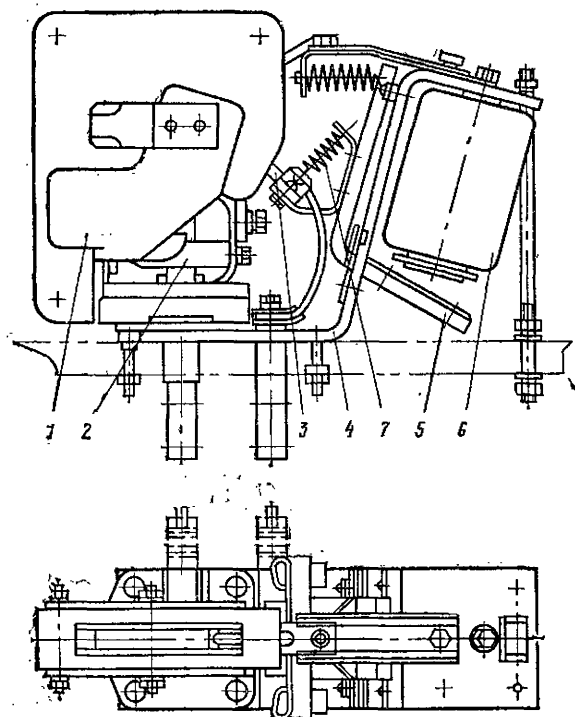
Общий вид контактора постоянного тока типа КПВ 603.
